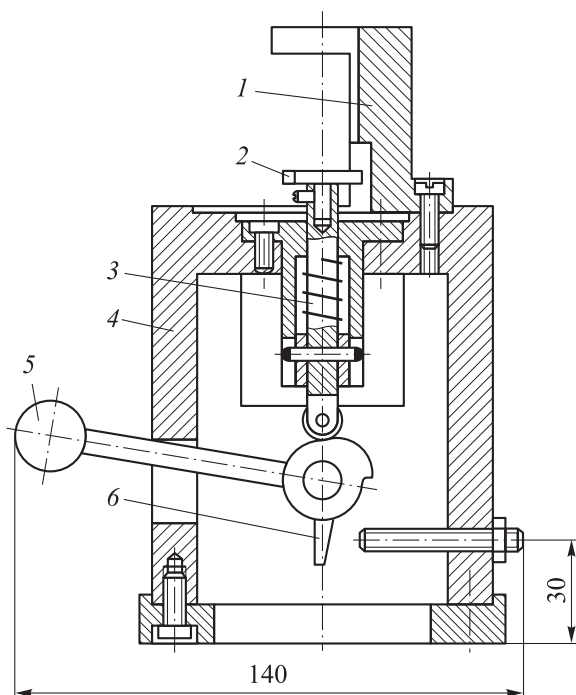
Схема устройства для регулирования статического сварочного давления и давления акустического контакта при УЗС:
